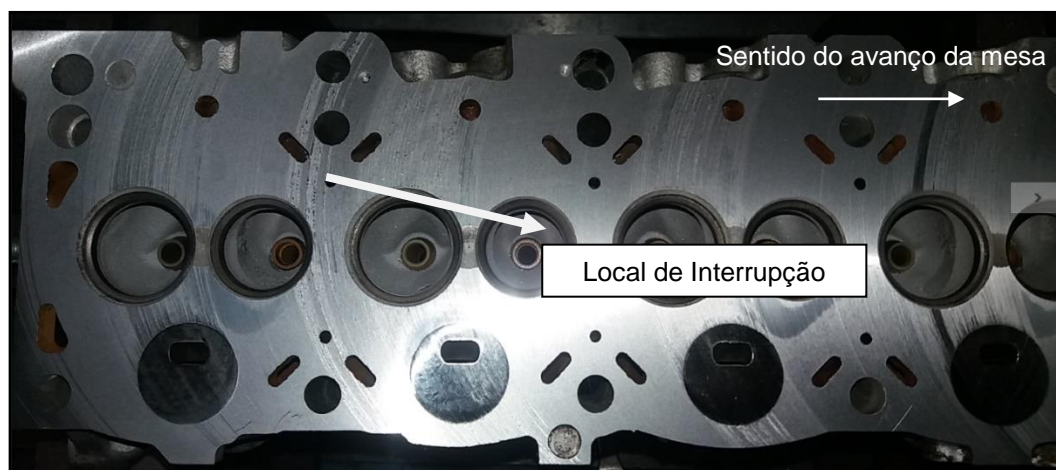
Cabeçote após usinagem com avanço de 20 mm/min.
